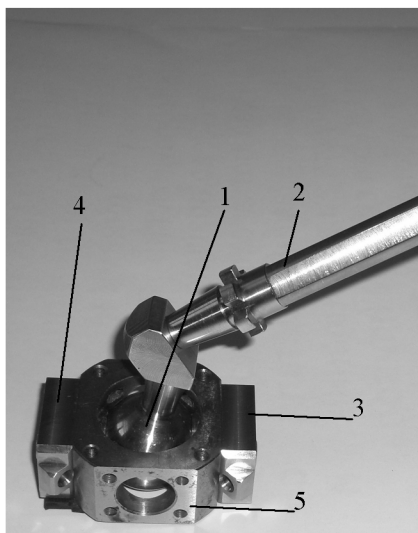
Розроблений сферичний шарнір просторової системи приводів
